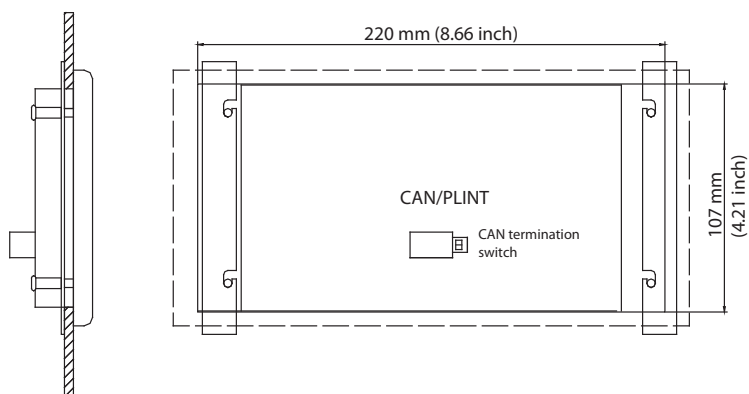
Bild till vänster, panelen monterad i en dörr. Bild till höger, panelen med plåtbleck sedd bakifrån med mått för öppningen.
